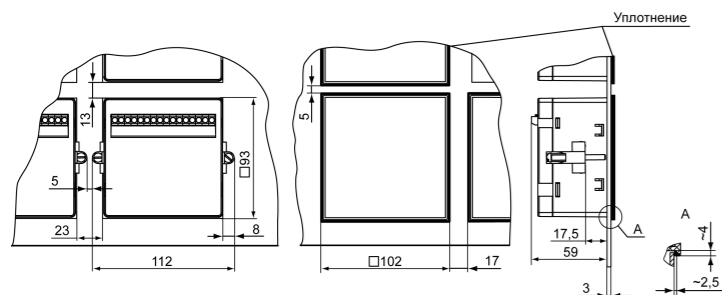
Прибор в корпусе Щ1, установленный в щит толщиной 3 мм
